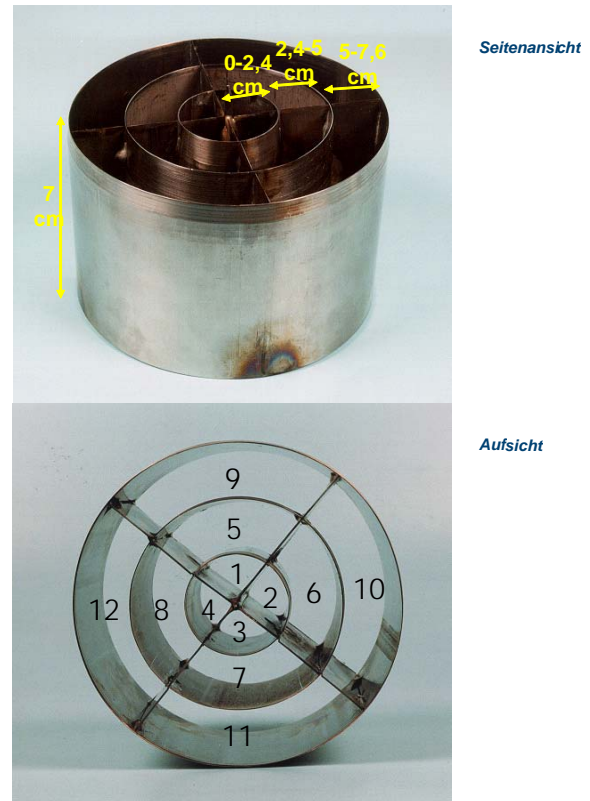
Werkzeug zum Zerteilen der beschossenen Gelatineblöcke entlang des Schusskanals in 12 Segmente
